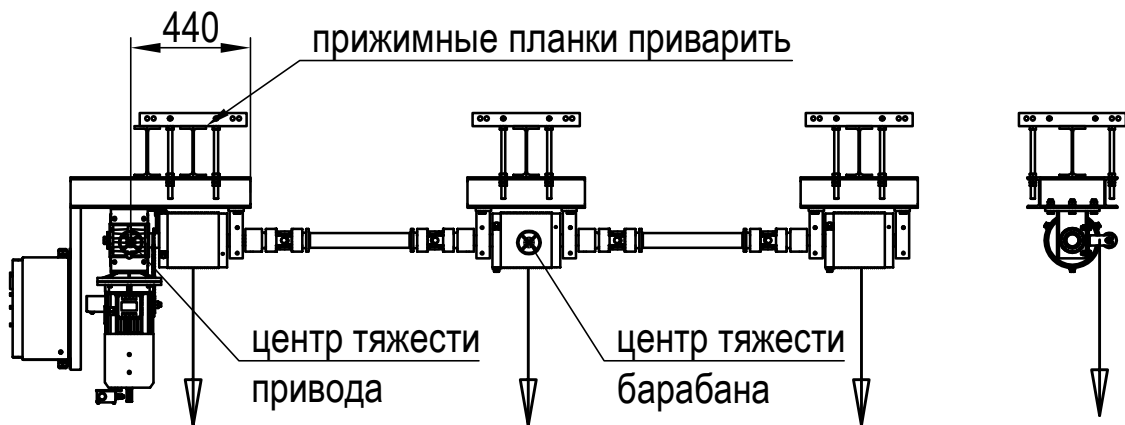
Возможный вариант крепления вальной лебедки прижимными планками к поперечным двутаврам
